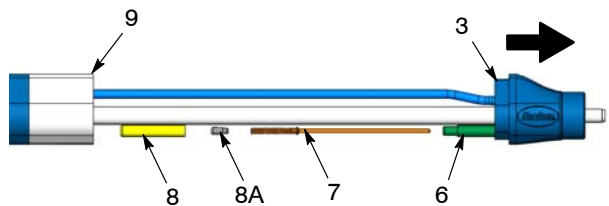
Démontage de la résistance – pistolets à fixation sur barre
